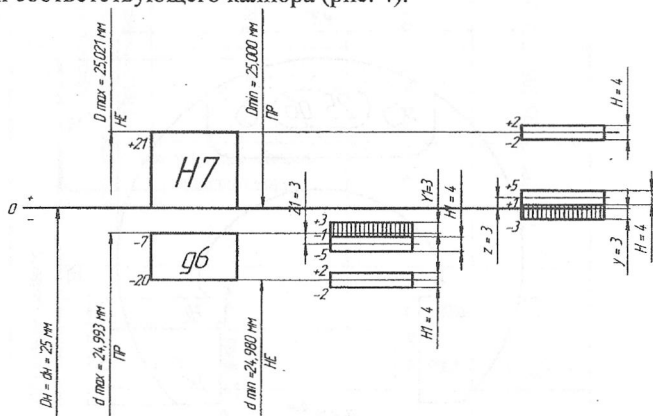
Схема расположения полей допусков соединения $\#25$ H7/g6, калибра-пробки (H) и калибра-скобы (H_1).
